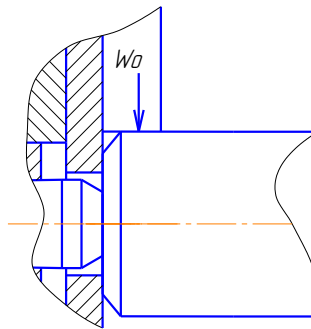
Схема для розрахунку зусилля, необхідного для затиску заготовки.
